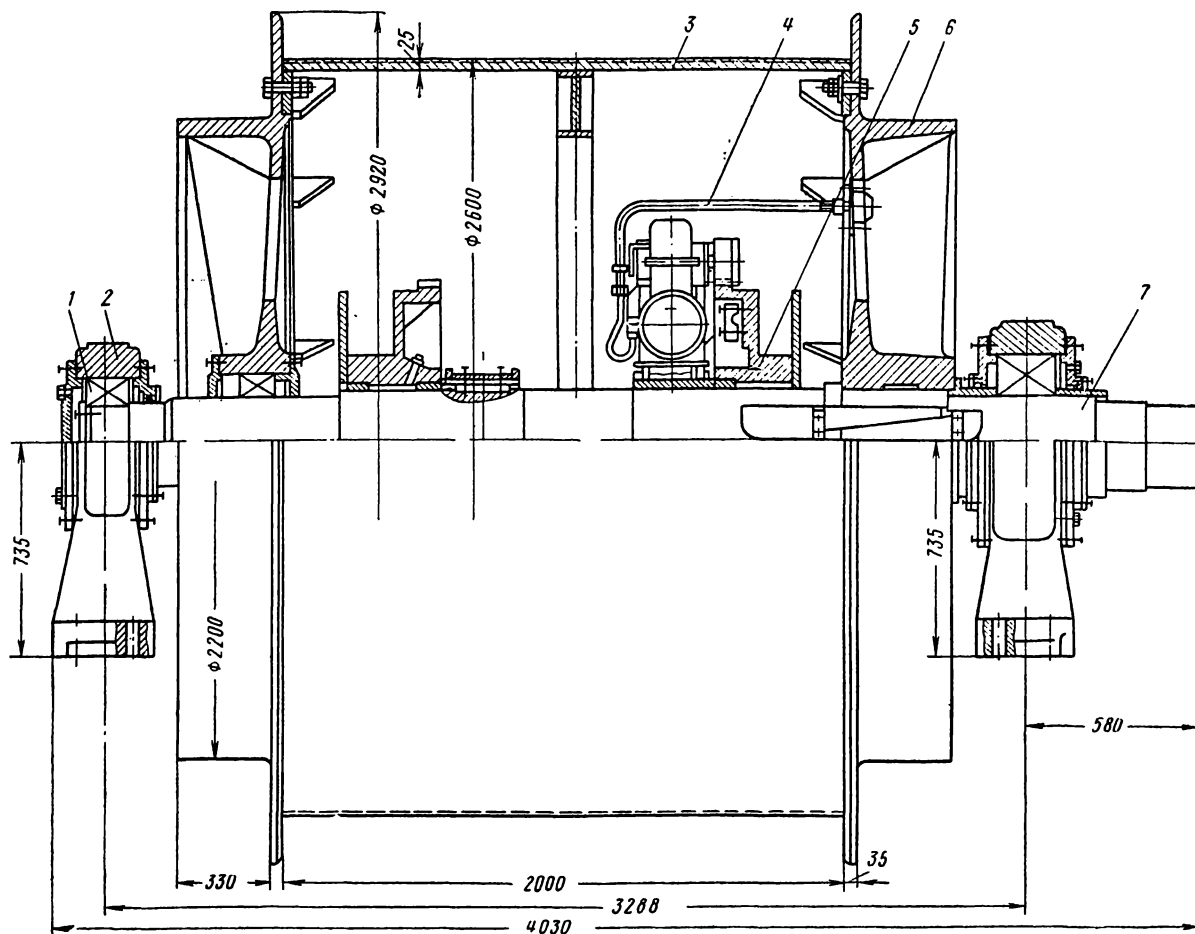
Сборка главного вала машины 1×2,5×2:
